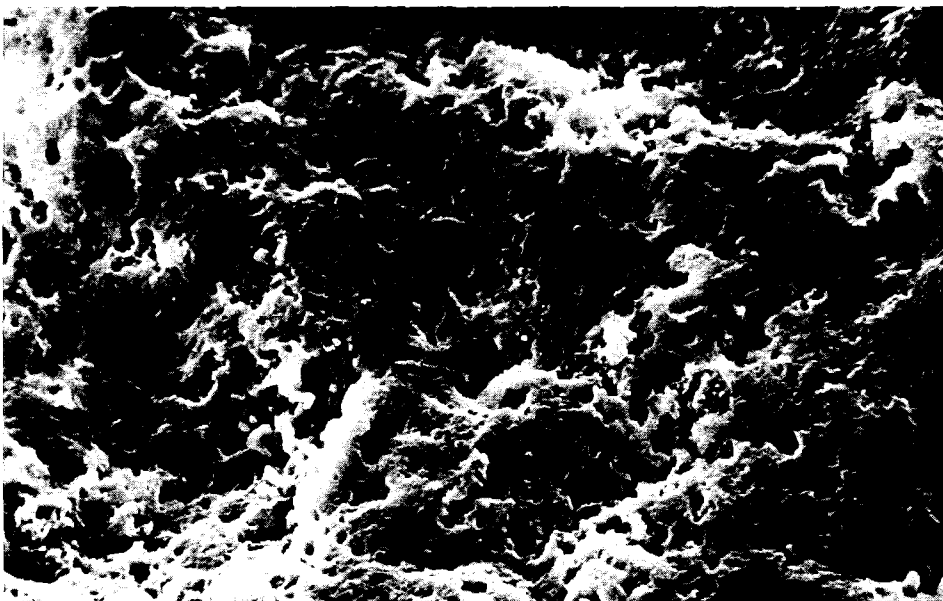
Kriechbruchfläche einer Probe (Material 3)
